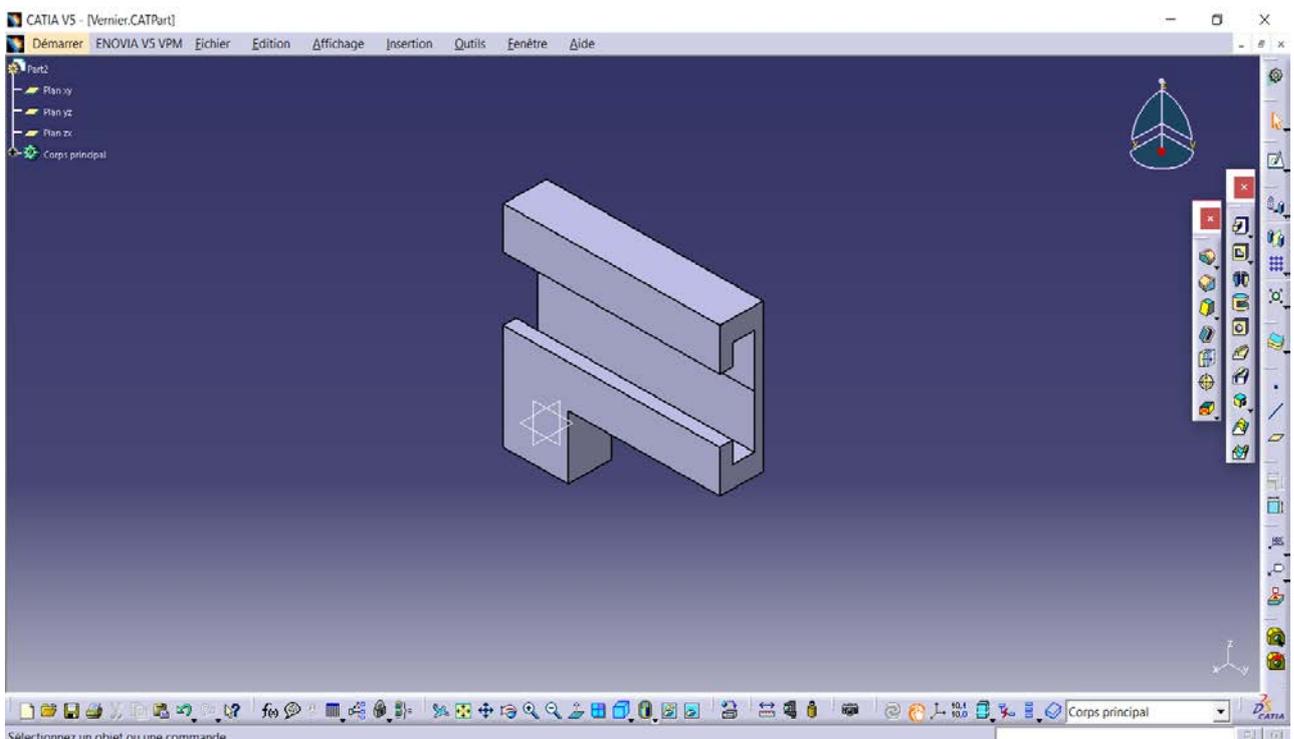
Part Design du Vernier de l'ensemble Pied à coulisse [1], [2]
